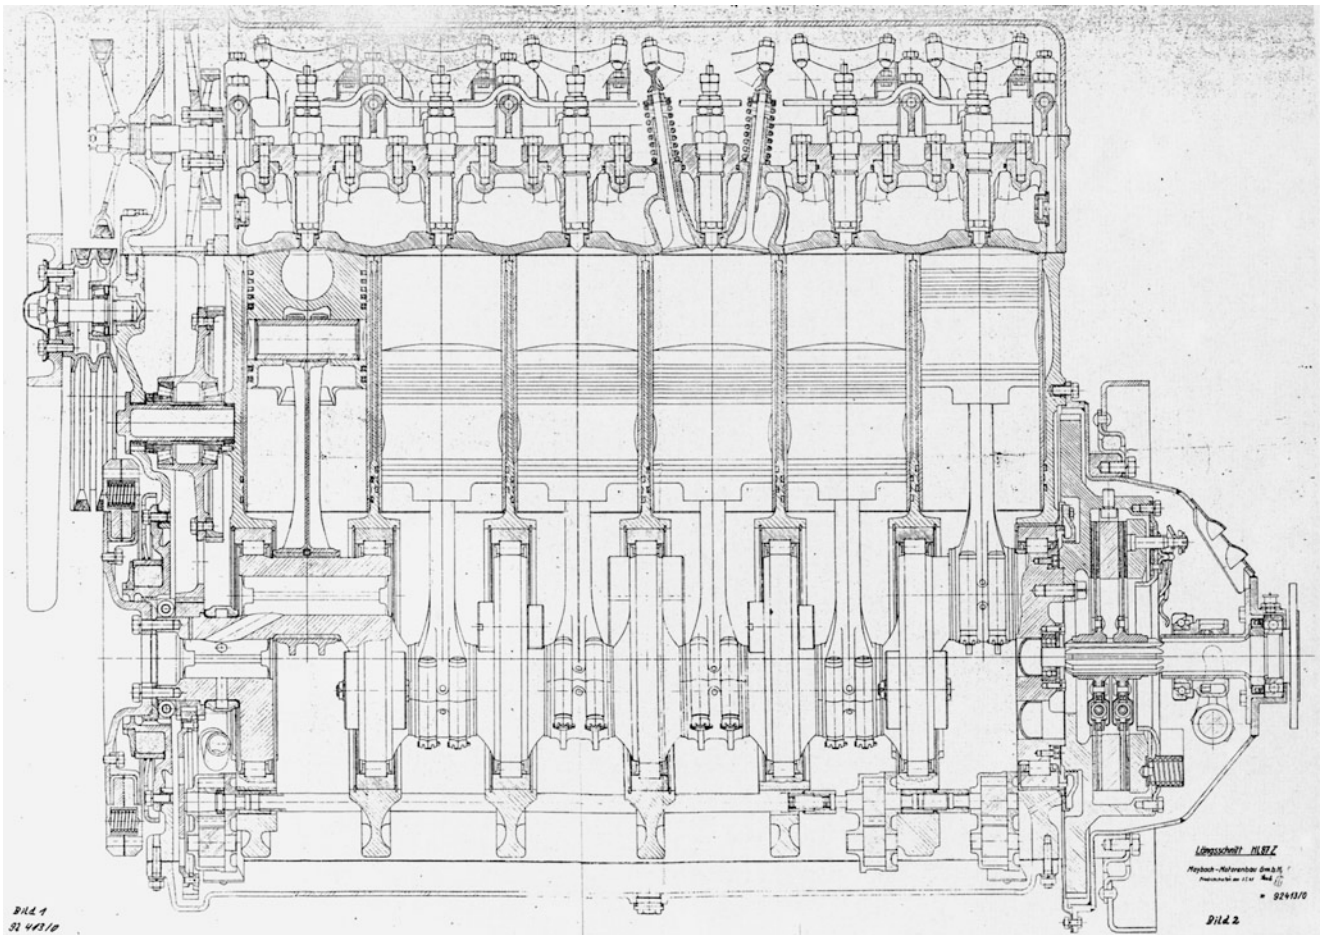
Längsschnitt des Versuchsmotors HL 87 (1941): wassergekühlter Viertakt-Dieselmotor mit direkter Einspritzung in Sechszylinder-Reihenbauart; Bohrung 125 mm, Hub 130 mm, Hubraum 9.567 cm³, Leistung 121 kW (165 PS) bei 2.400 min⁻¹
